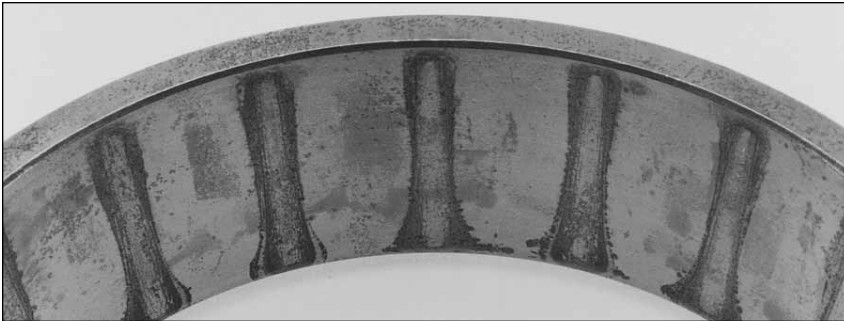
Las estrías horizontales provocan un contacto incorrecto de la rodadura y reducen la vida útil del rodamiento.
